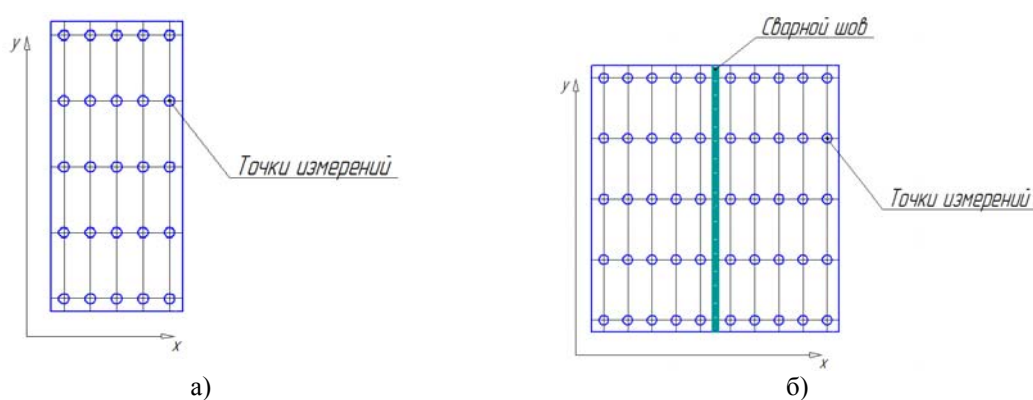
Схема измерений напряжений: а) до сварки; б) после сварки
